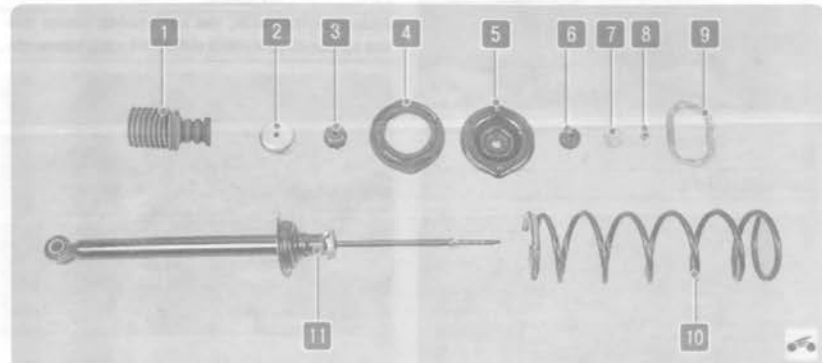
Детали задней амортизаторной стойки: 1 – защитный чехол; 2 – тарелка буфера сжатия; 3 – буфер сжатия; 4 – верхняя прокладка пружины; 5 – верхняя опора крепления амортизаторной стойки; 6 – резиновая втулка; 7 – шайба верхней опорной чашки пружины; 8 – гайка штока амортизатора; 9 – прокладка верхней опоры; 10 – пружина; 11 – амортизатор
